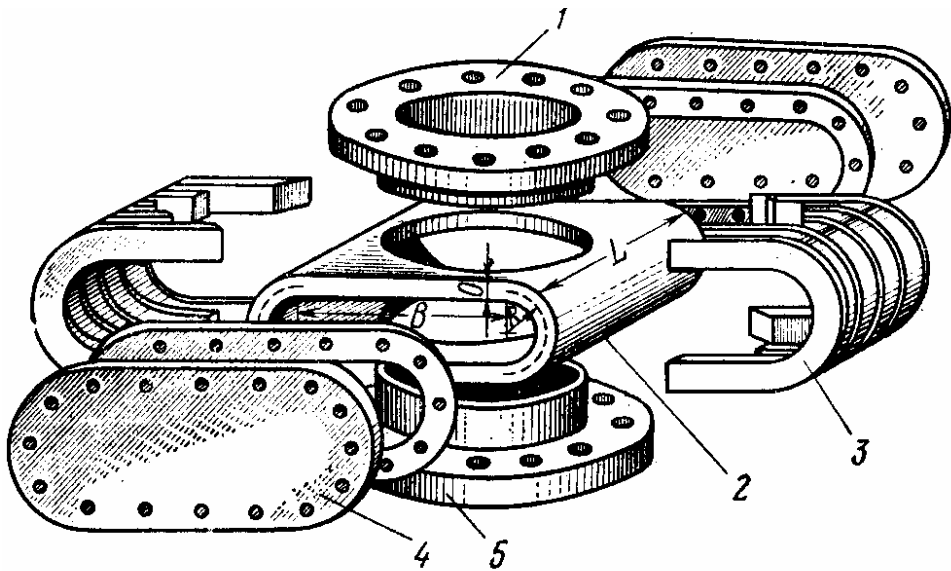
Элементы конструкции корпуса плащечного преветора
